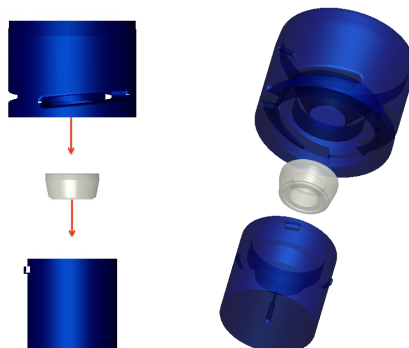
Componenti del bioreattore in vista laterale (a sinistra) e in vista 3D (a destra). Le frecce rosse indicano come inserire le varie componenti per serrare il patch nella camera di coltura.
